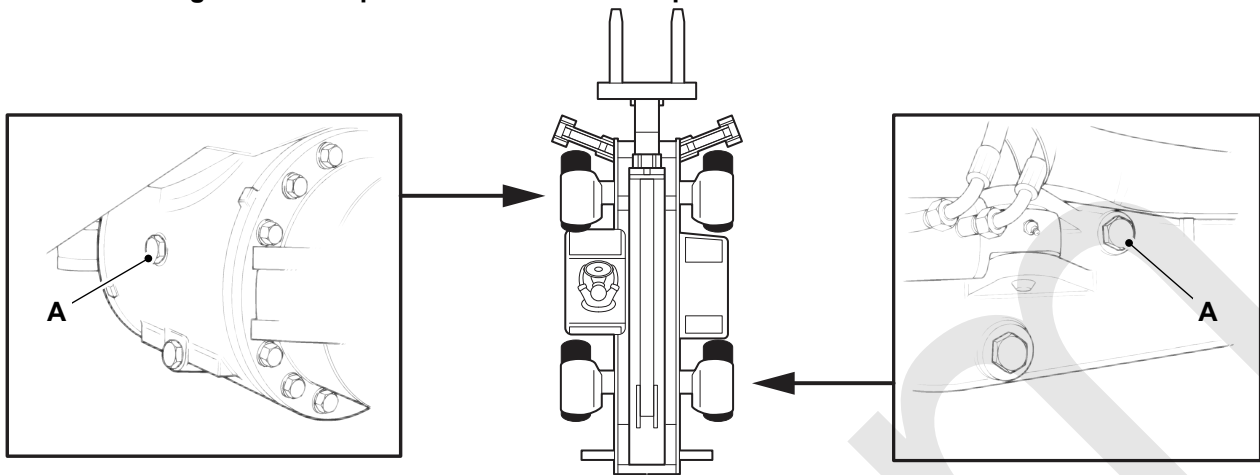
Máquinas con barras de acoplamiento transversal accionadas
